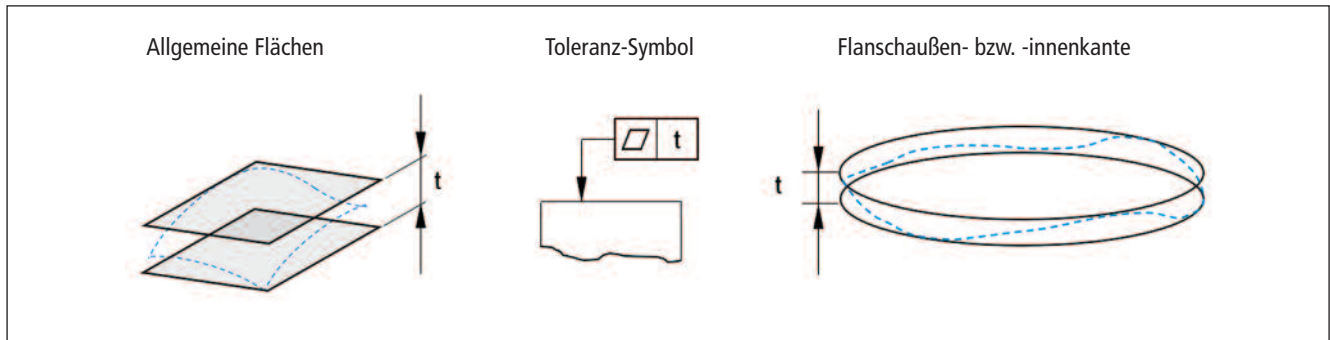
Ebenheitstoleranz für Flächen allgemein und für Flansche entlang der Außen- oder Innenkante
